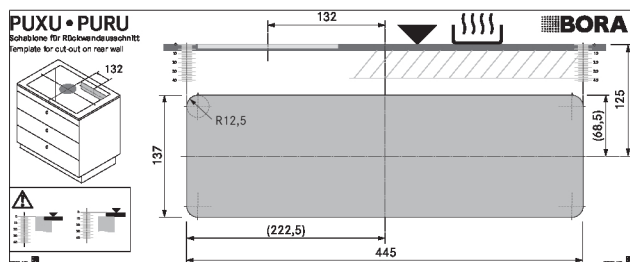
Dimenzije vgradnje pri obtočnem zraku, različica montaže A
